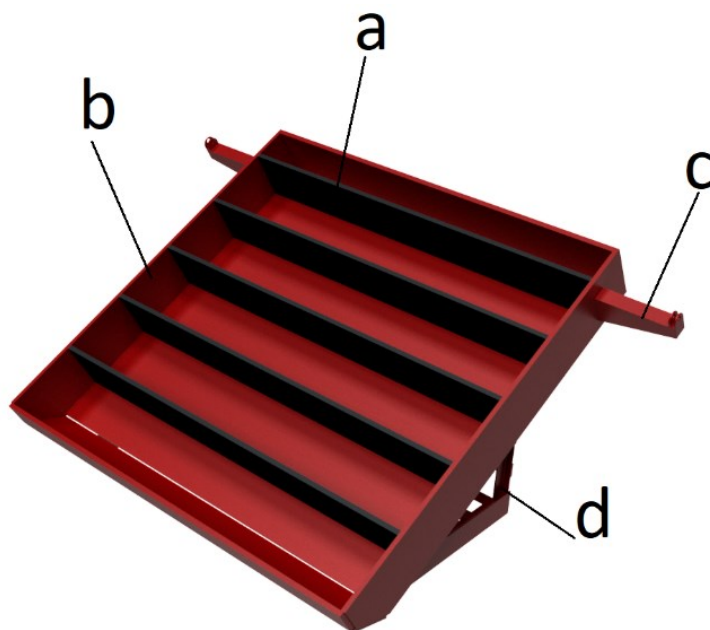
1. řešení konstrukce ve sklopeném stavu
